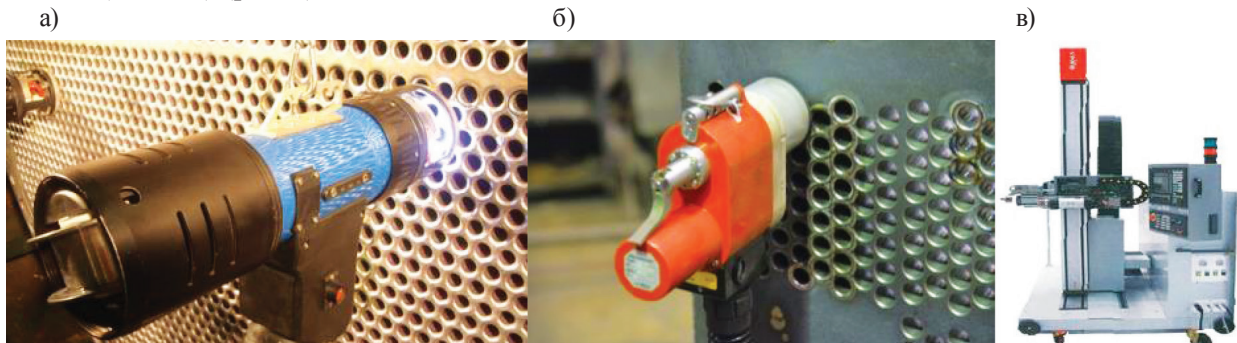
Оборудование для сварки трубных решеток:
